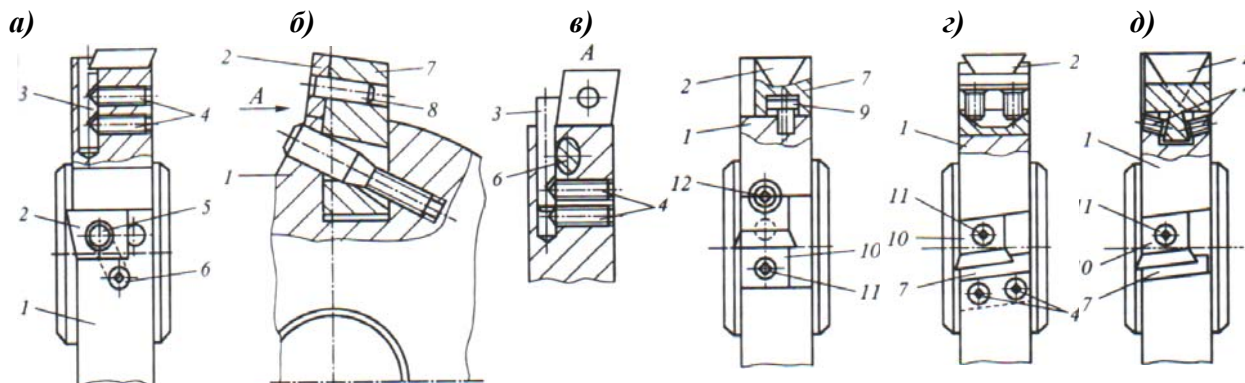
Сборные дисковые фрезы ведущих фирм мира, с регулируемым креплением СМП
